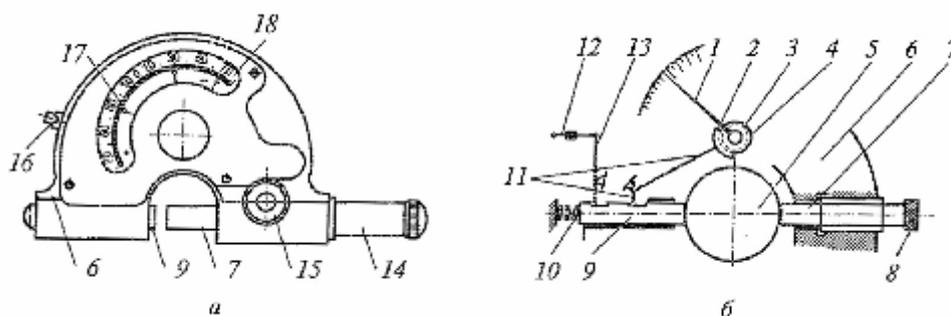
Рычажная скоба-пассамстр (а) и ее схема (б): 1 – стрелка; 2 – зубчатый сектор; 3 – спиральная пружина; 4 – зубчатое колесо; 5 – объект измерения; 6 – корпус; 7 – неподвижная (регулируемая) пятка; 8 – микровинт для настройки; 9 – подвижная пятка; 10 – пружина; 11 – измерительный рычаг; 12 – стержень арретира; 13 – рычаг арретира; 14 – предохранительный чехол; 15 – гайка фиксатора; 16 – кнопка арретира; 17 – шкала; 18 – указатель предела действительных отклонений
